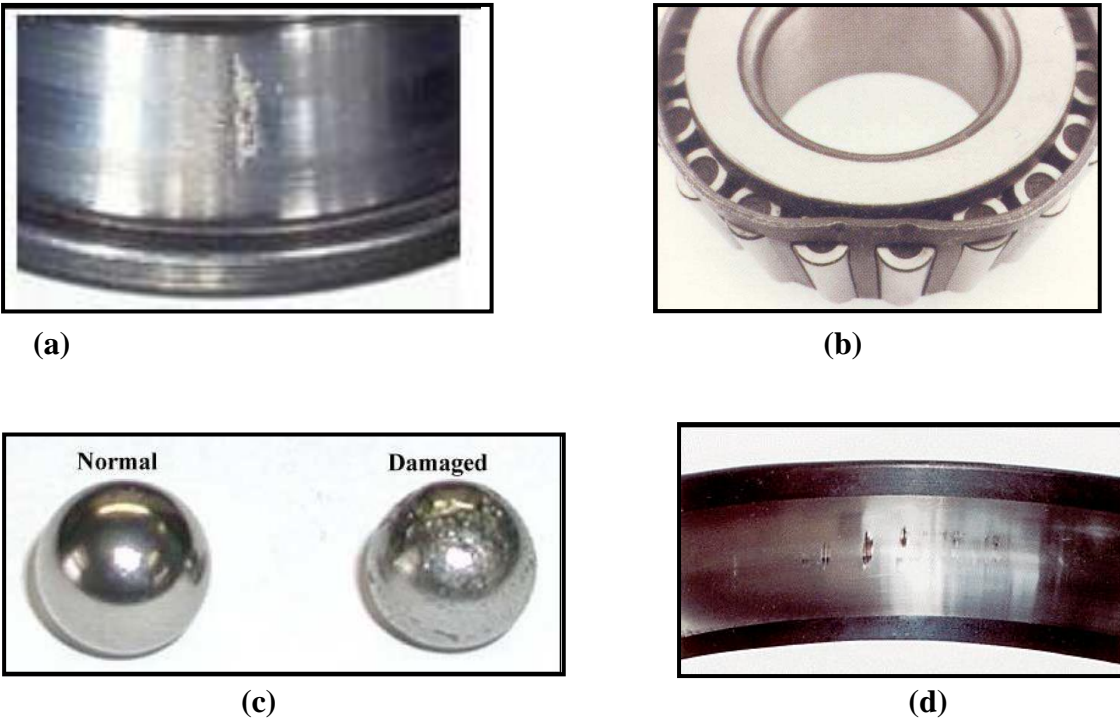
Défauts des roulements à billes. (a) sur la bague interne; (b) sur la cage; (c) sur une bille et (d) sur la bague externe [3].
